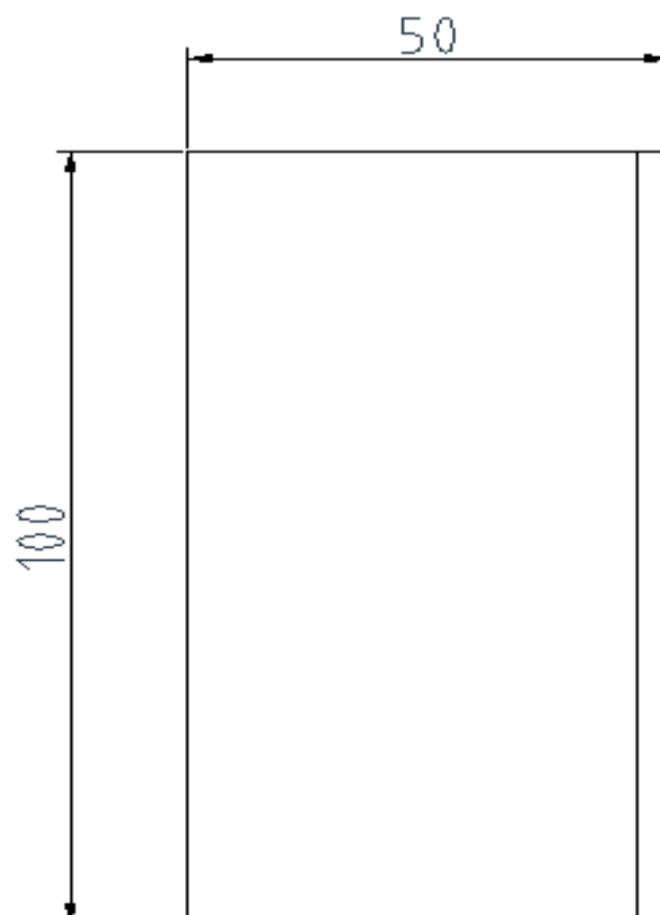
Medidas en milímetros de placas para ser soldadas
